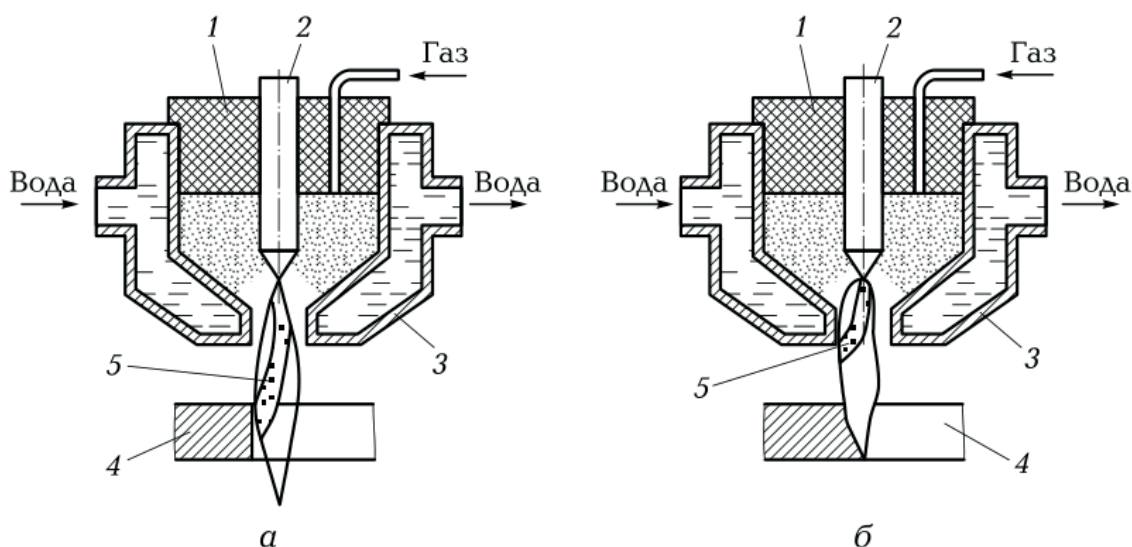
Схеми плазматронів прямої (а) і непрямої (б) дії: 1 – ізолятор; 2 – неплавкий електрод; 3 – сопло плазматрона; 4 – зварювана деталь; 5 – стиснута дуга
